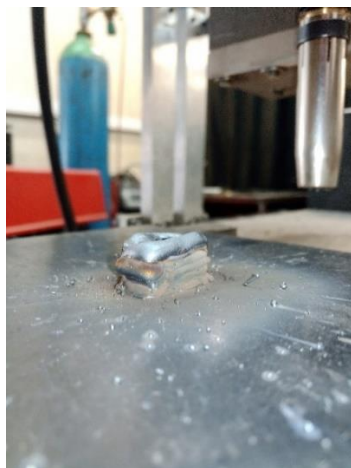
Vista em plano frontal da soldadura 3D
